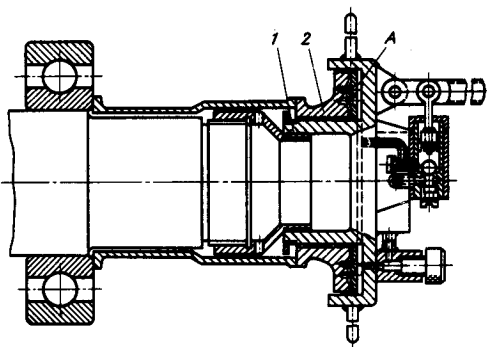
Гидравлическое приспособление для напрессовки крупногабаритного подшипника
